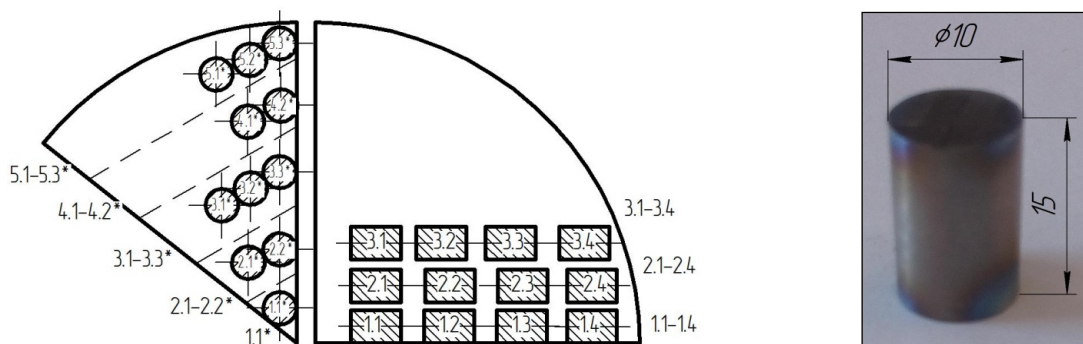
Схема отбора образцов из темплетов заготовок из титанового сплава марки ПТ-1М и фотография образца с размерами
